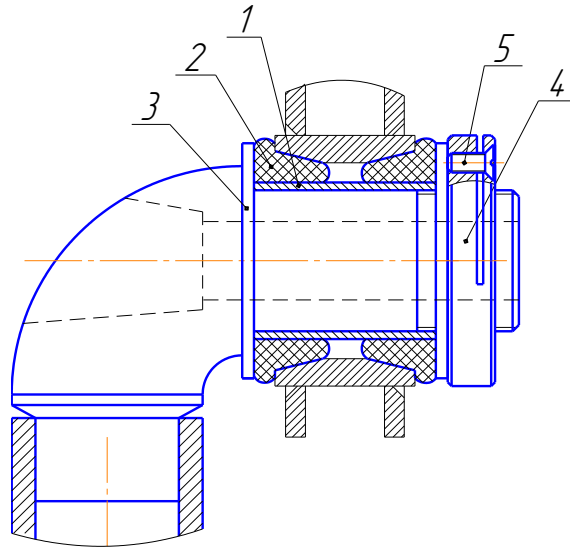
Схема шарнірного вузла для з'єднання повздовжнього рычага підвіски з рамою причепа.
